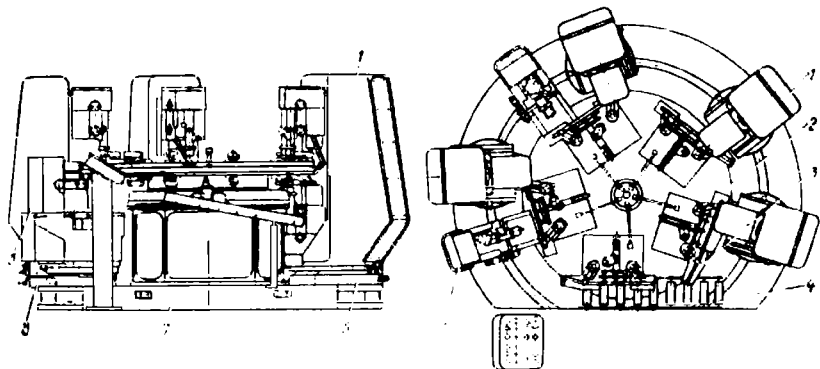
Схема сверлильно-фрезерного станка СТ409:
